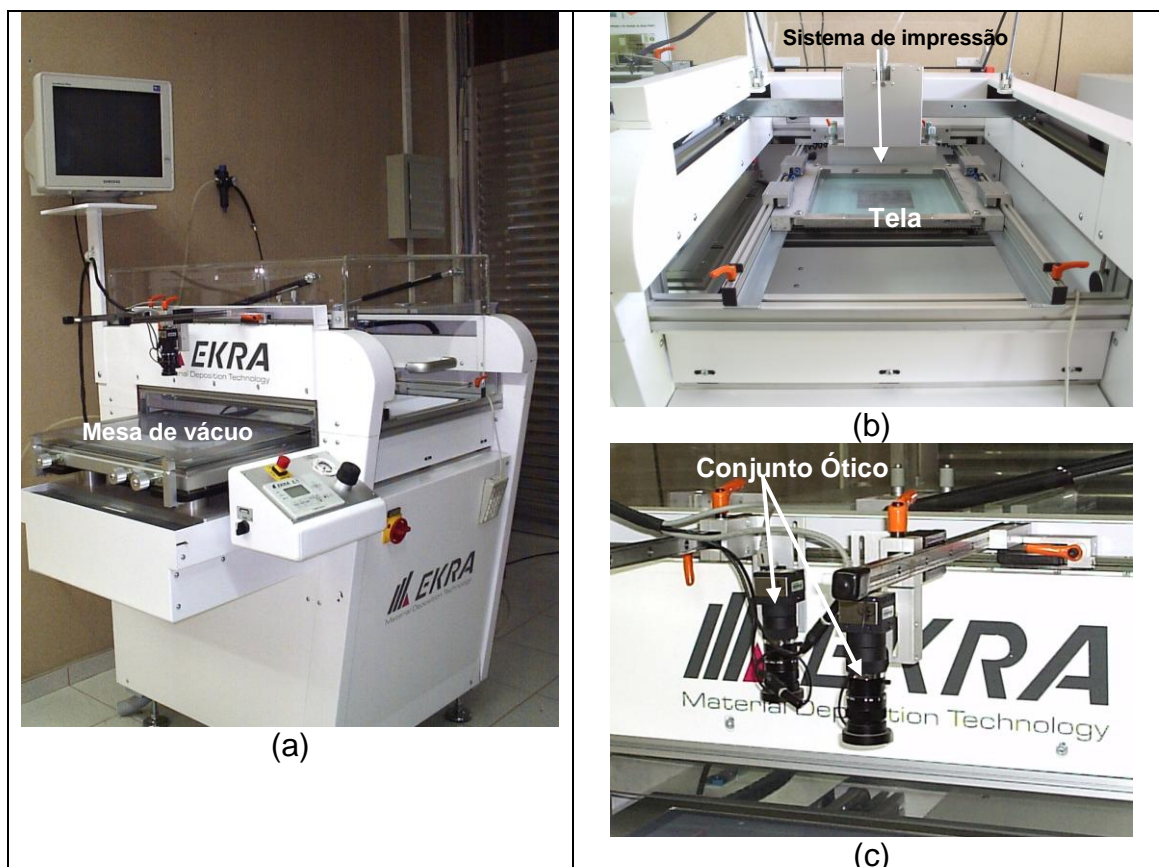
Máquina de impressão à tela. (a) visão geral, (b) detalhe da tela, sistema de impressão e mesa de vácuo e (c) detalhe do conjunto ótico.
